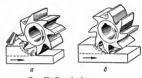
Способы фрезерования: а — против подачи (встречное фрезерование); 6 — по подаче (попутное фрезерование).
